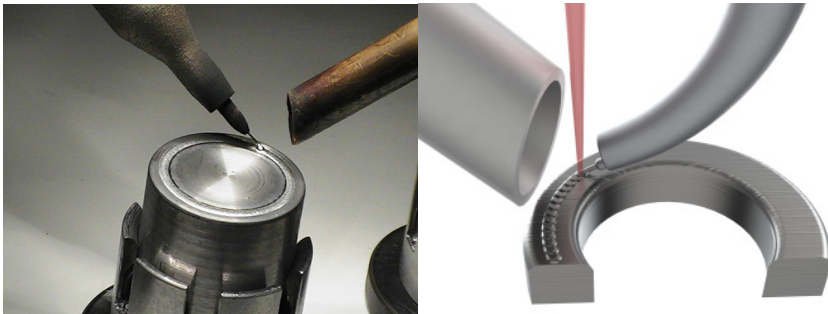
Auftragschweißprozess mit EUTECT-SWF
